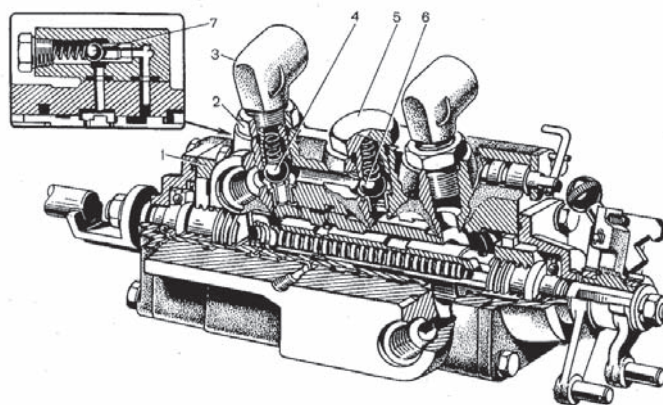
Силовой (позиционный) регулятор. 1 — корпус; 2 — контргайка; 3 — поворотный угольник; 4, 6, 7 — клапана; 5 — пробка
